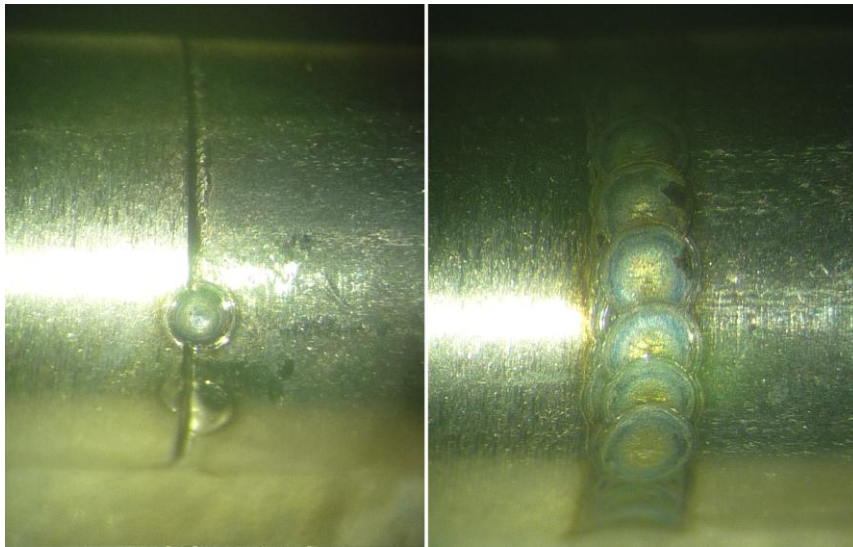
Detalle de una de las piezas con soldadura láser, se observa la realización de un punto “bueno” y otro “fallado” abajo (Izquierda) y la soldadura completa entre ambas piezas (Derecha).
